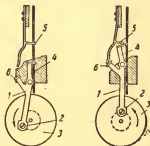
Схема грейферного механизма камеры 16С-1:
